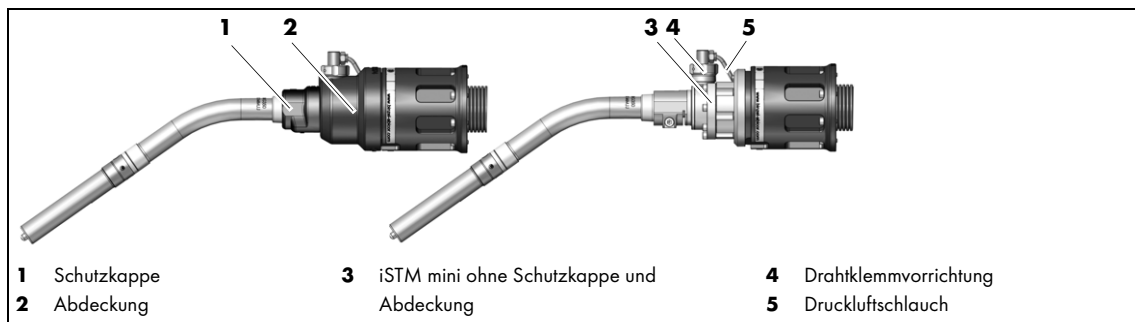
Reinigung iSTM mini für ABIROB® G mit Wire-Brake
